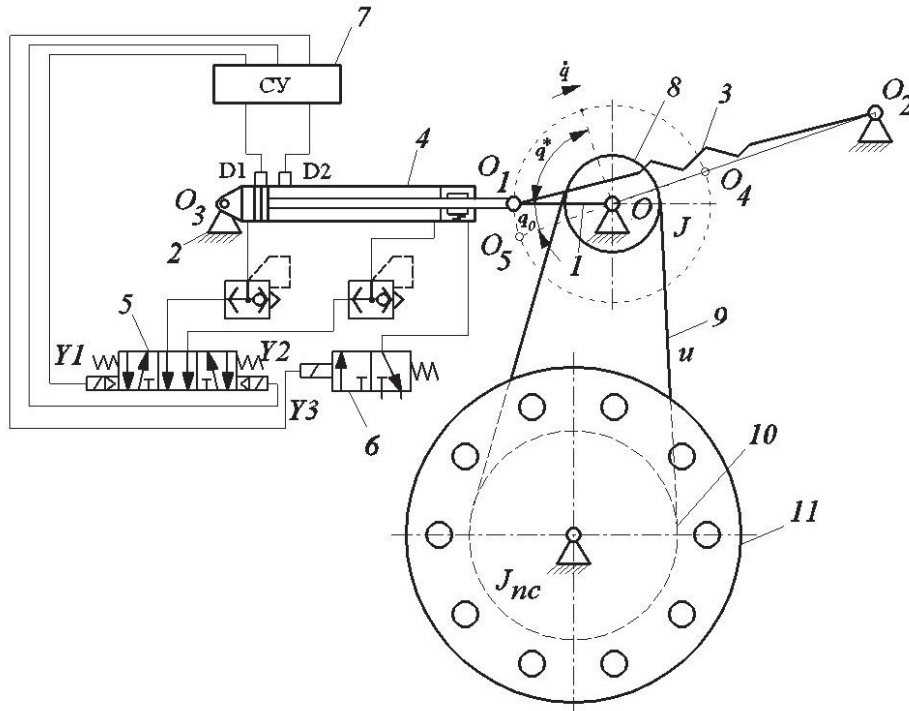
Кинематическая схема неререверсивного пружинного шагового привода: 1 – поворотное звено; 2 – основание; 3 – пружина; 4 – пневматический цилиндр; 5 – распределитель 5/3; 6 – распределитель 3/2; 7 – система управления; 8 – ведущий шкив зубчатой ременной передачи; 9 – зубчатый ремень; 10 – ведомый шкив зубчатой ременной передачи; 11 – поворотный стол
